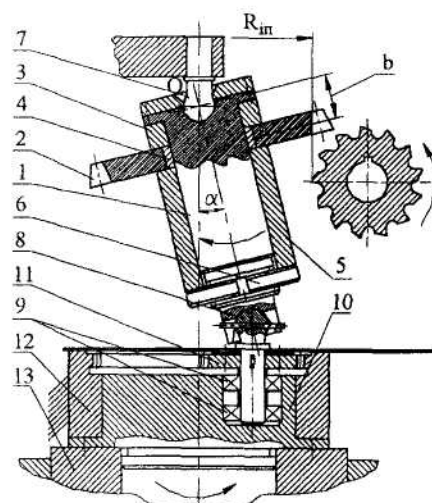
Схема пристрою для обробки зубів сателіта для зубофрезерного верстата: 1 - оправка; 2 - заготовка; 3, 4, 5 - втулки; 6 - гайка; 7, 8 - універсальні шарніри; 9 - підшипники; 10 - водило; 11 - сателіт пристрою; 12 - центральне зубчасте колесо пристрою; 13 - гвинти; O - центр прецесії;  $R_{in}$  - настроювальний розмір
